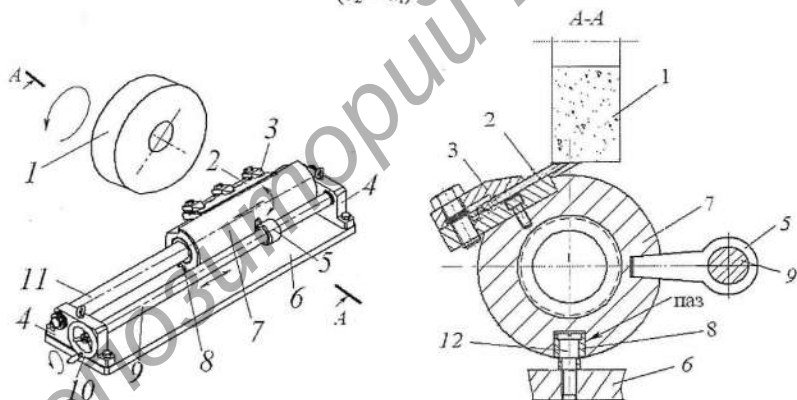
Принципиальная схема устройства: 1 — шлифовальный круг, 2 — нож, 3 — прихват, 4 — опора с подшипниками, 5 — гайка, 6 — основание, 7 — барабан, 8 — ролик, 9 — ходовой винт, 10 — маховичок, 11 — направляющая барабана, 12 — кронштейн
